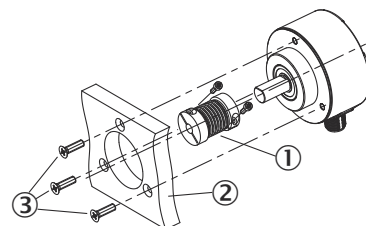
Anbau Servoflansch über flanschseitige Gewindebohrungen
